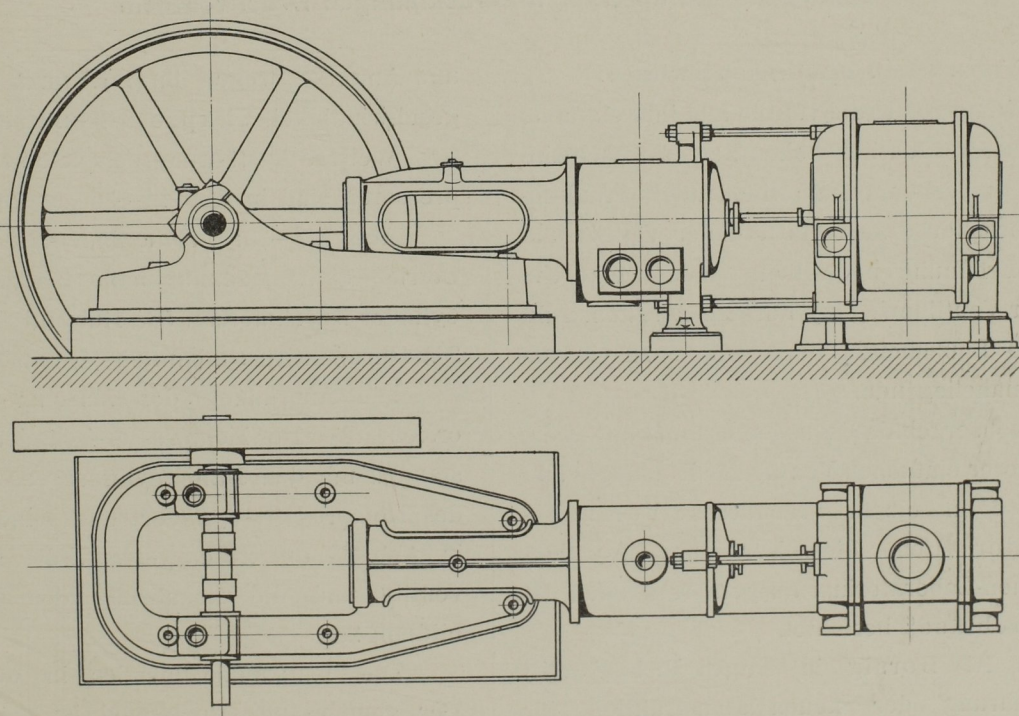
Seitenansicht und Grundriss. Massst. 1:30.
